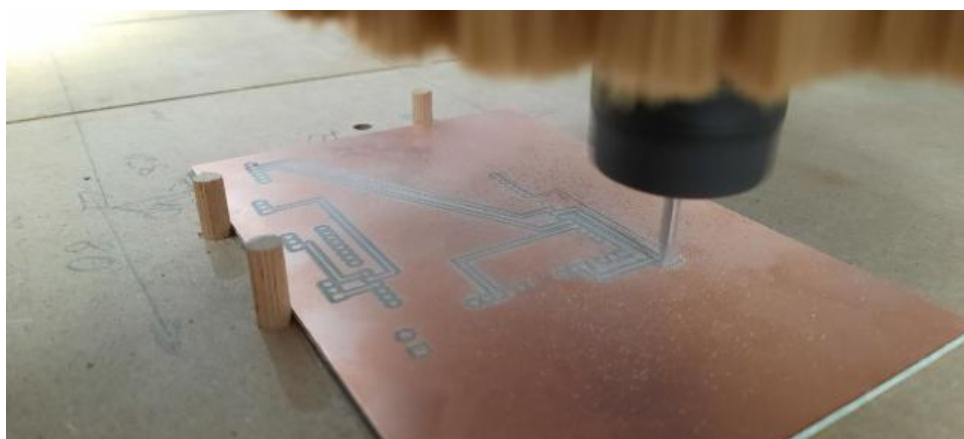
Фрезеровка платы на ЧПУ станке
